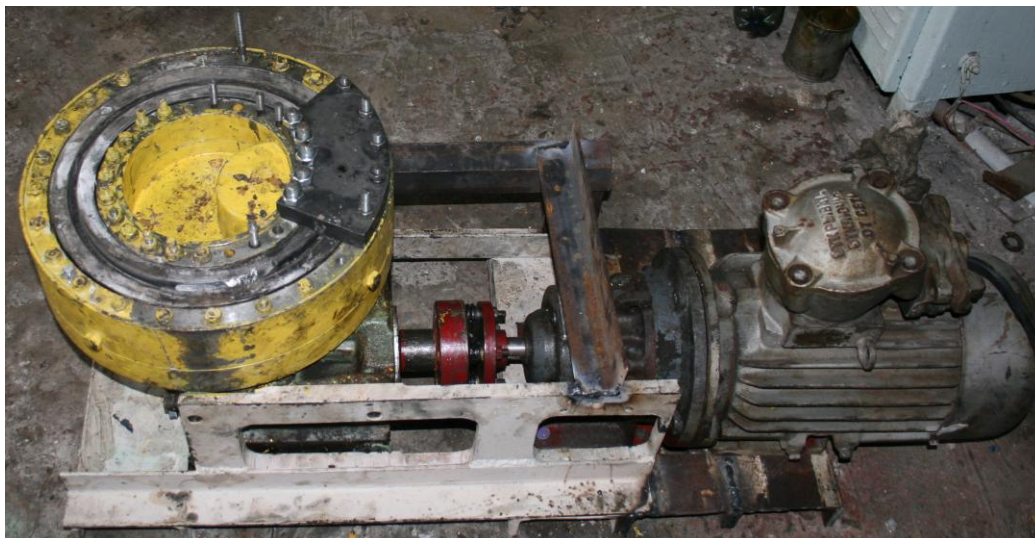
Опытная установка непрерывного литья-прессования металла.
